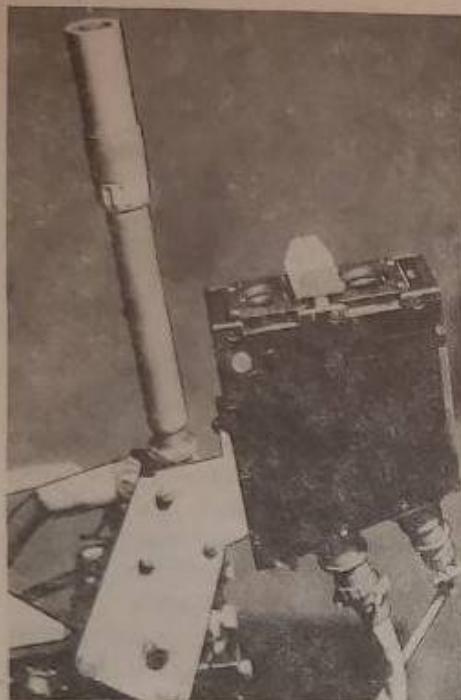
Оптический сенсор ОС-3, размещенный на горелке робота для дуговой сварки
